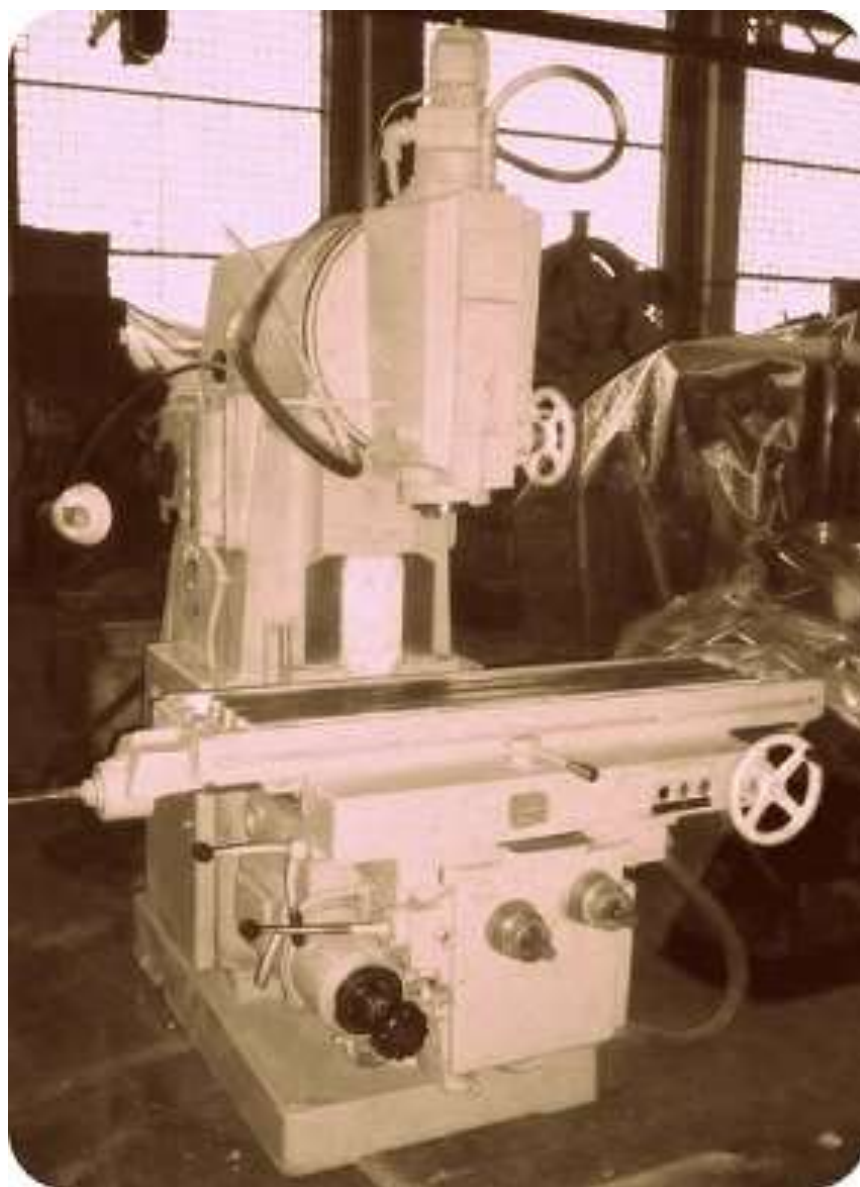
Вертикально-фрезерный станок 6P12
